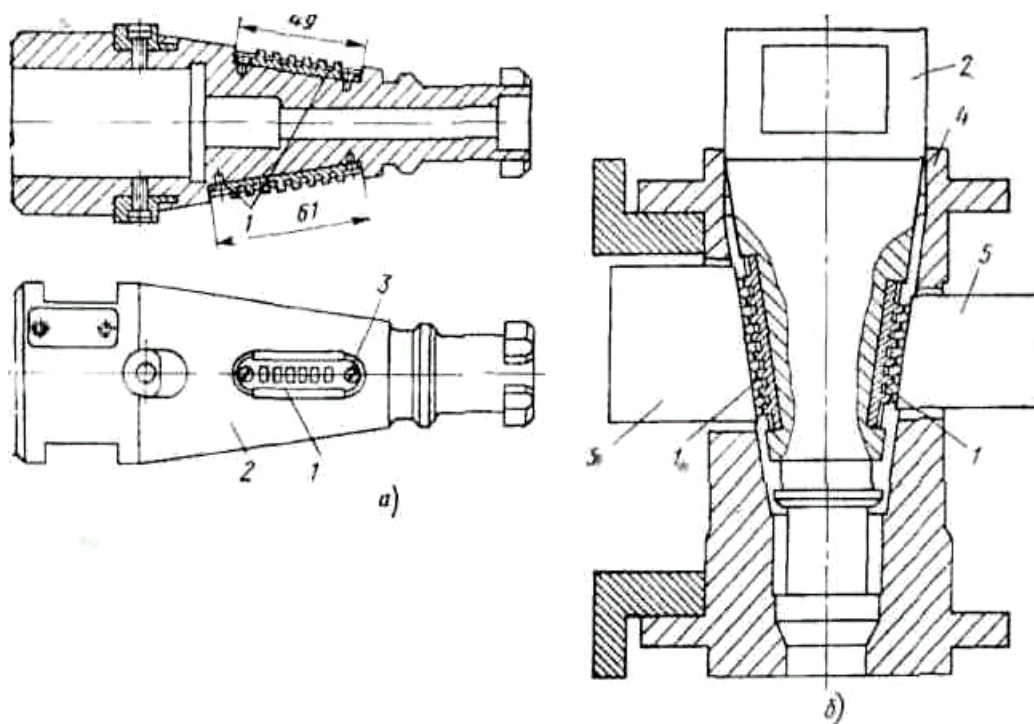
Інструментальні оправки з кодovими гребінками
